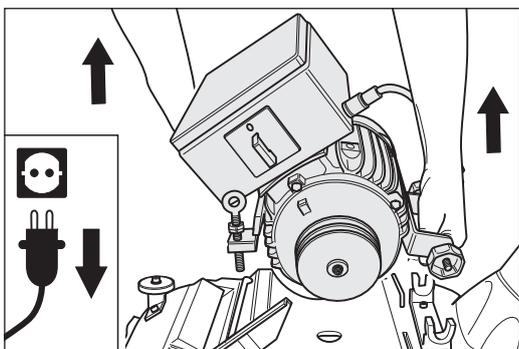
Den Motor vom Maschinengehäuse abnehmen.
